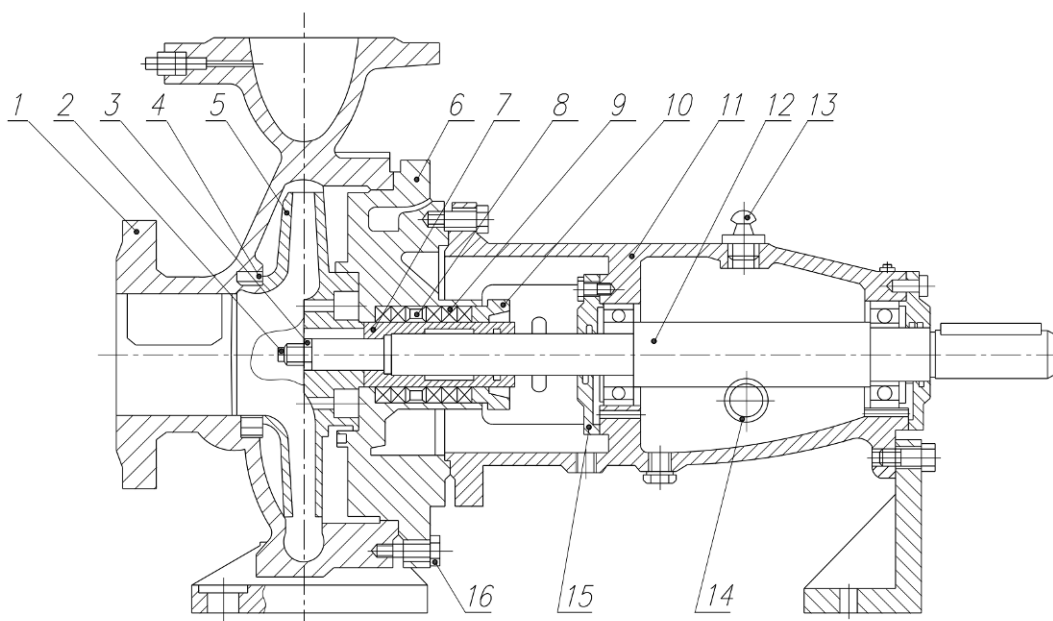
Схема конструкції консольного насоса: 1 – корпус; 2 – гайка робочого колеса; 3 – стопорна шайба; 4 – ущільнення корпусу; 5 – робоче колесо; 6 – кришка корпусу з корпусом ущільнення; 7 – захисна втулка; 8 – кільце сальника; 9 – сальникова набивка; 10 – кришка сальника; 11 – корпус підшипників із опорним кронштейном; 12 – вал; 13 – отвори для заливання оливи; 14 – контрольне вікно; 15 – кришки підшипників; 16 – гайки кришки корпусу.
